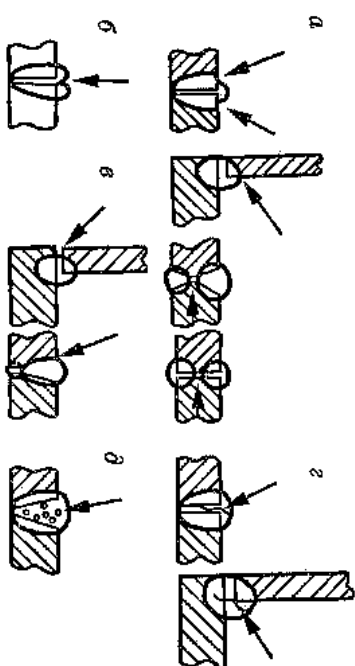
Дефекты сварных соединений (стрелками указан дефект)
